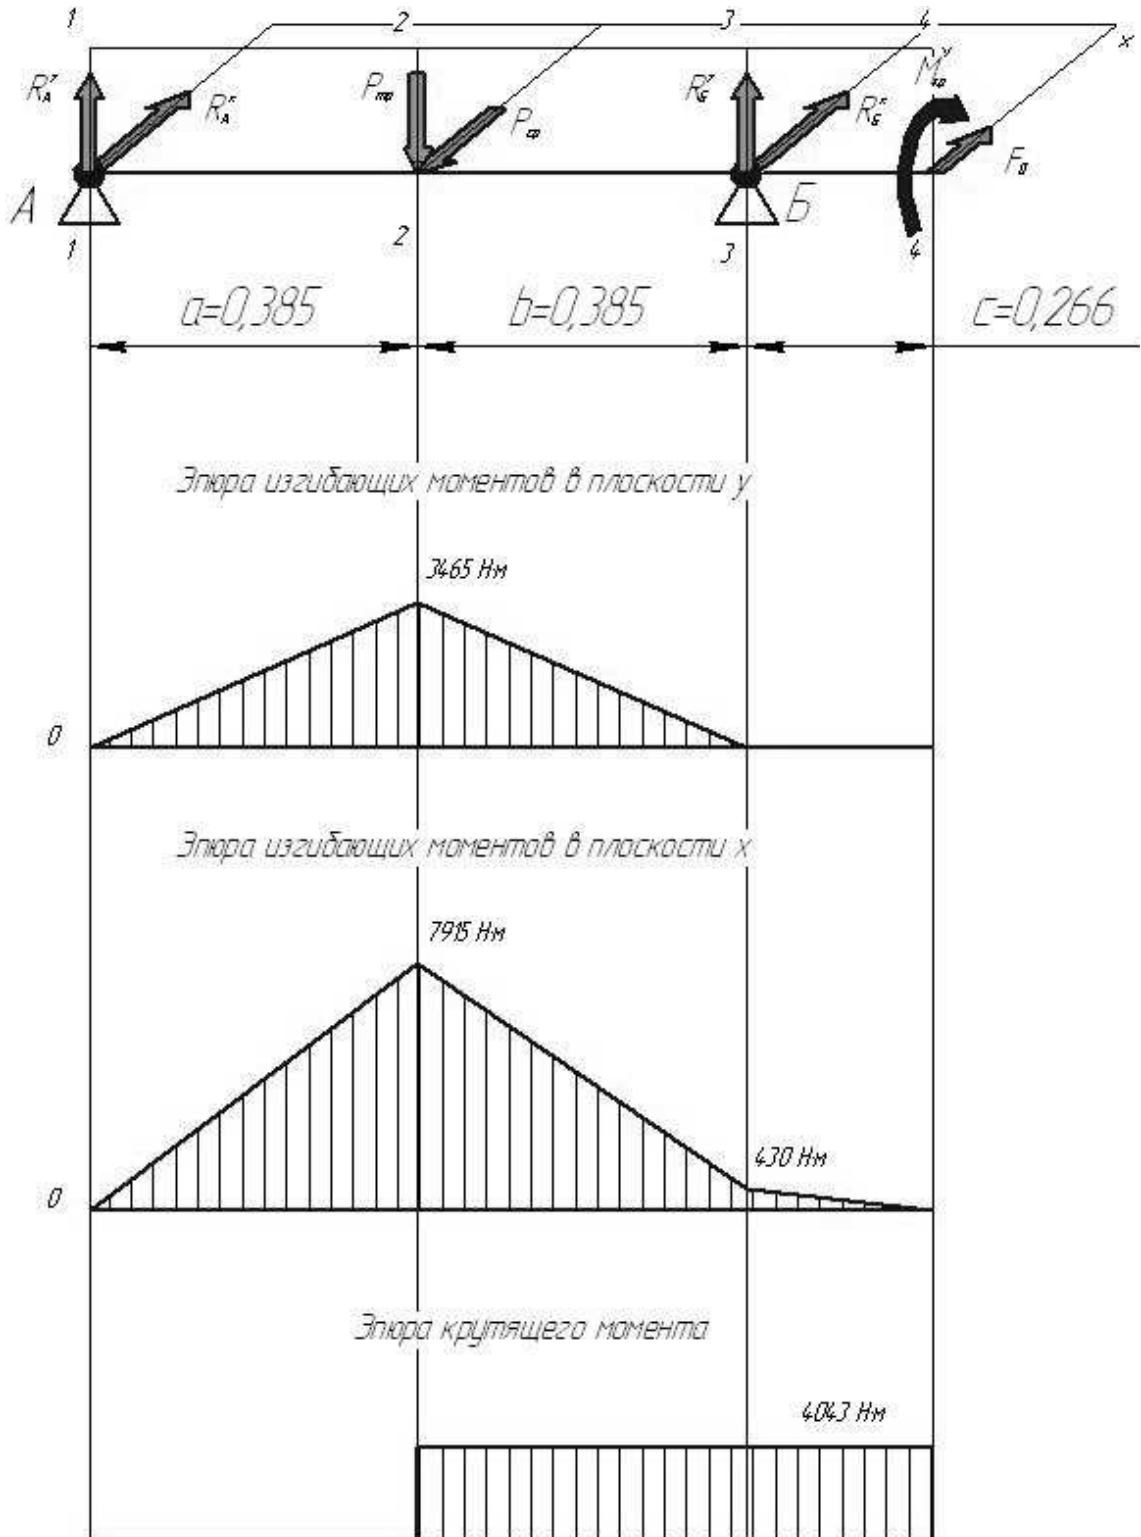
Розрахункова схема приводного вала дробарки з епюрами згинальних і крутних моментів
